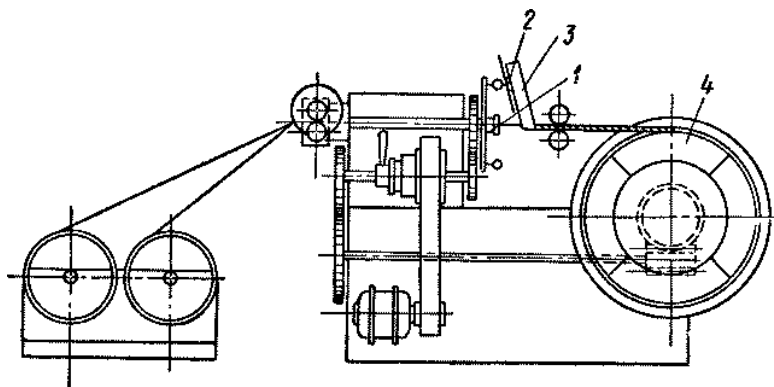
Кинематическая схема станка для наложения витковой микалентной изоляции.
